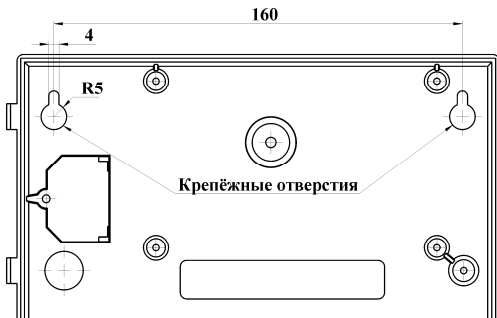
Установочный чертёж корпуса (вид изнутри)
